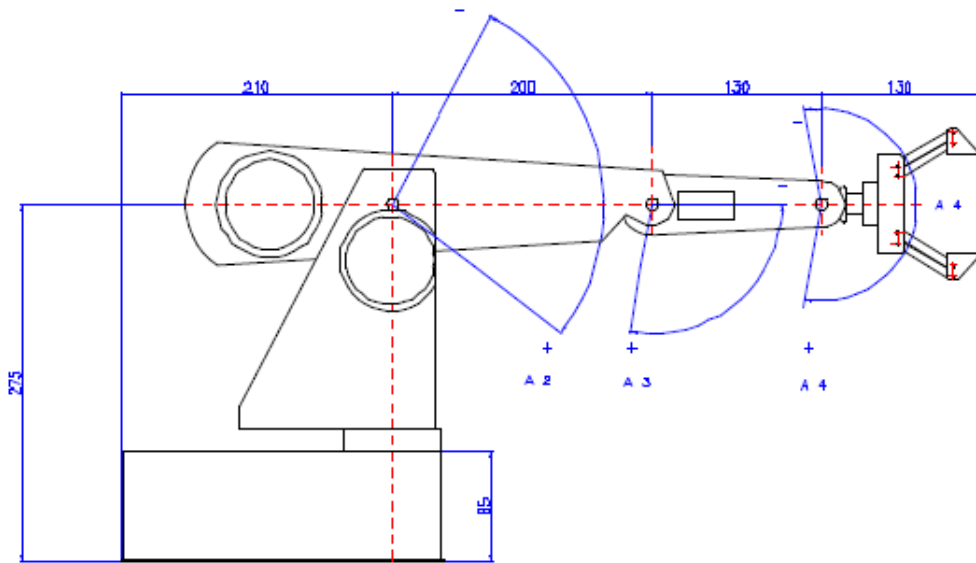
Les dimensions du robot *ROB3* (vue de face).
